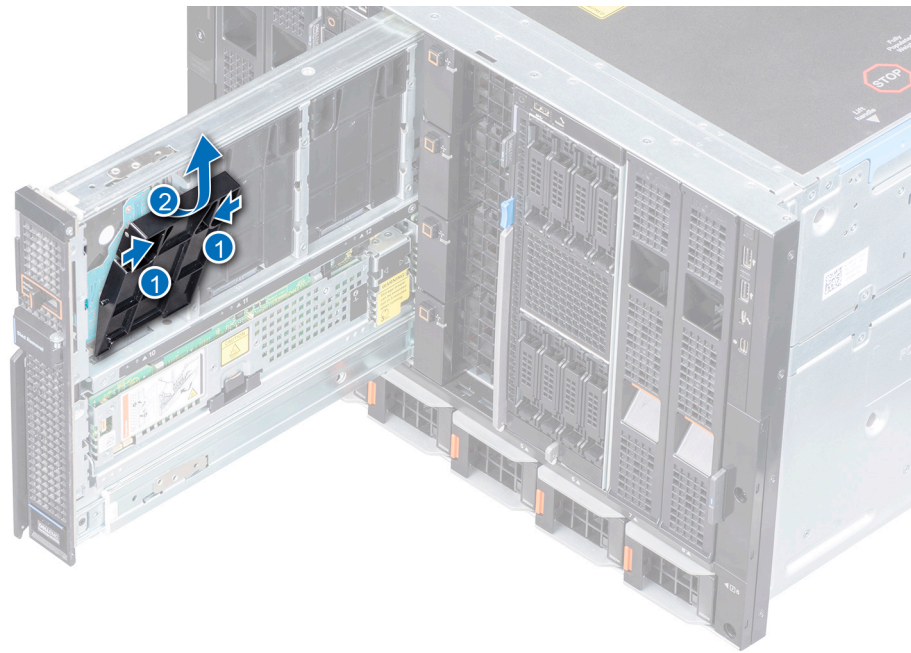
Entfernen eines Laufwerkplatzhalters
